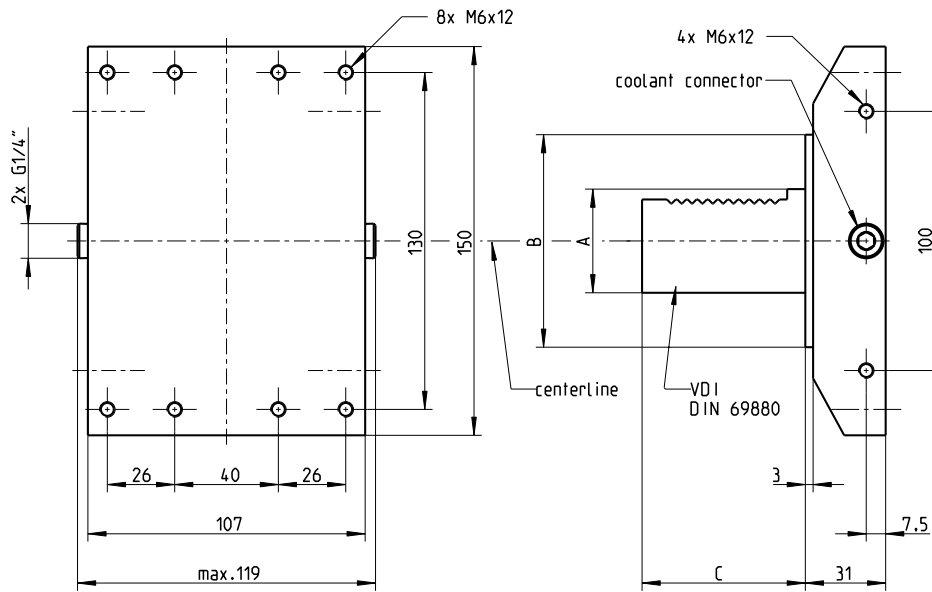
Maschinenadapter mit Zylinderschaft für Scheibenrevolver mit VDI-Werkzeugaufnahme, Typ 9129AB...
